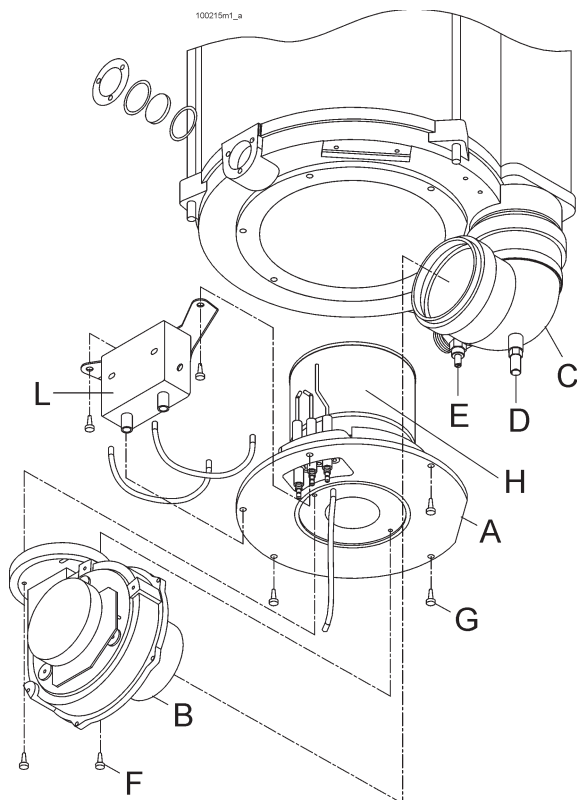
Smontaggio parte inferiore scambiatore di calore
